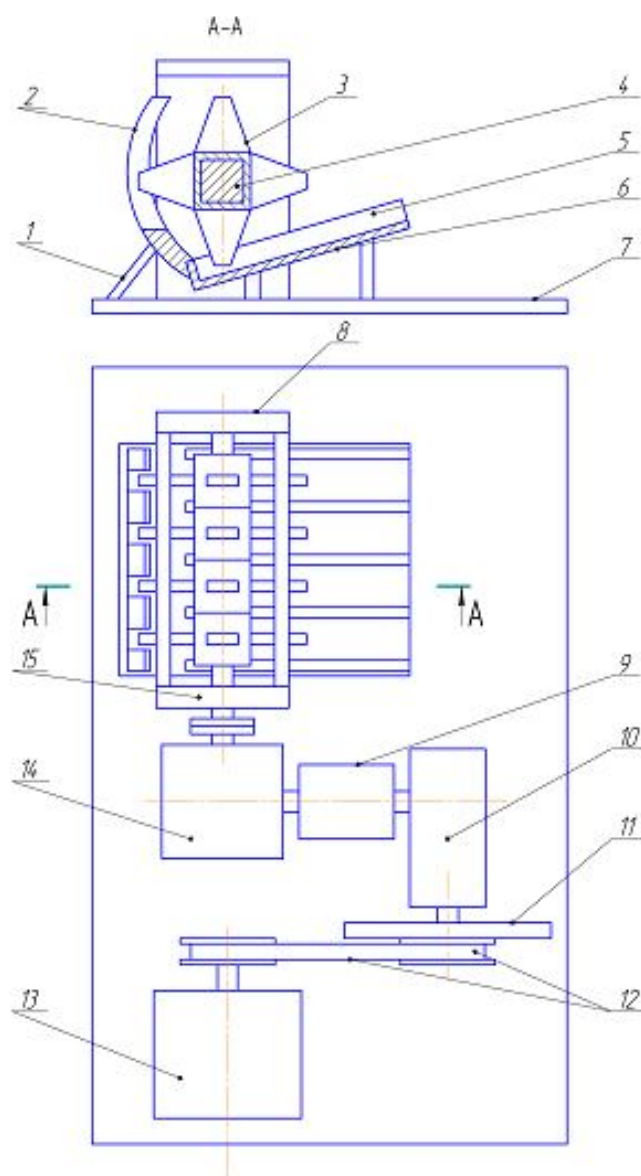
Схема лабораторной одновалковой зубчатой дробилки
